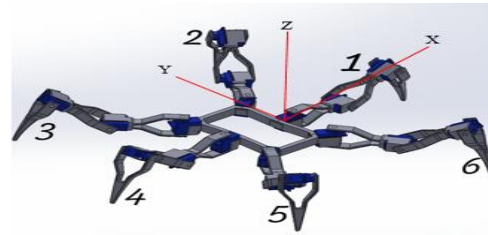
Vista isométrica de robot hexápodo. Fuente: Propia
